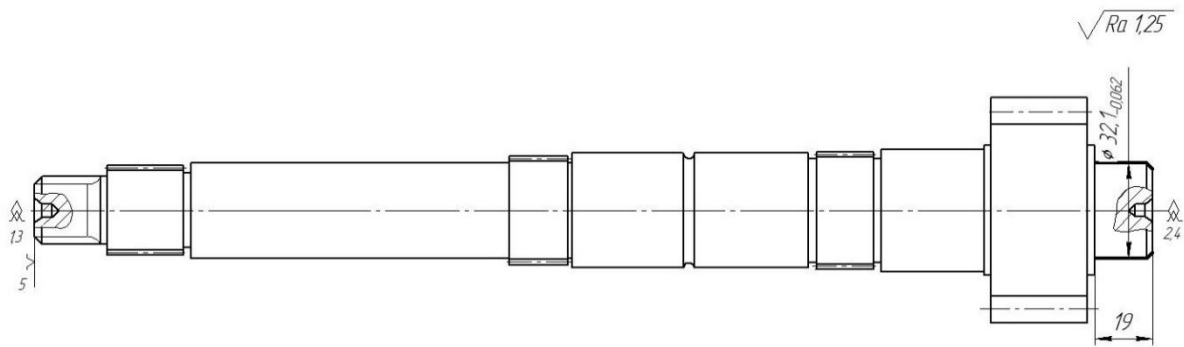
Схема базування вала під час остаточного шліфування опорної шийки.
